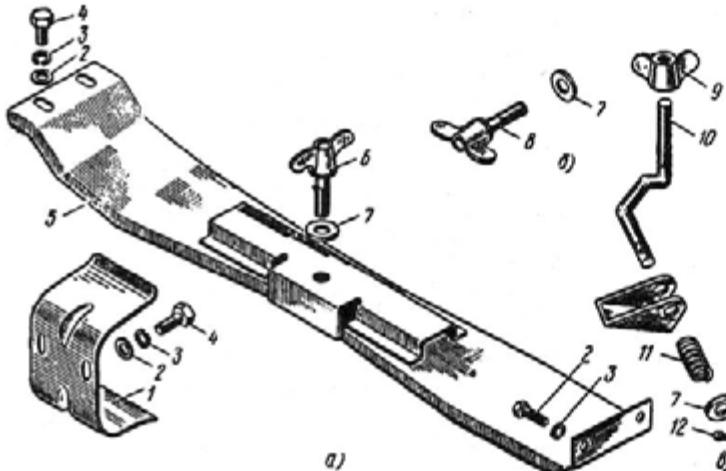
Держатель запасного колеса: а — для кузова «универсал»; б — для кузова «фургон»; в — для кузова «седан»
